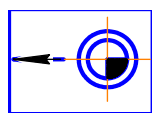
Положение заготовки в рабочем пространстве станка
